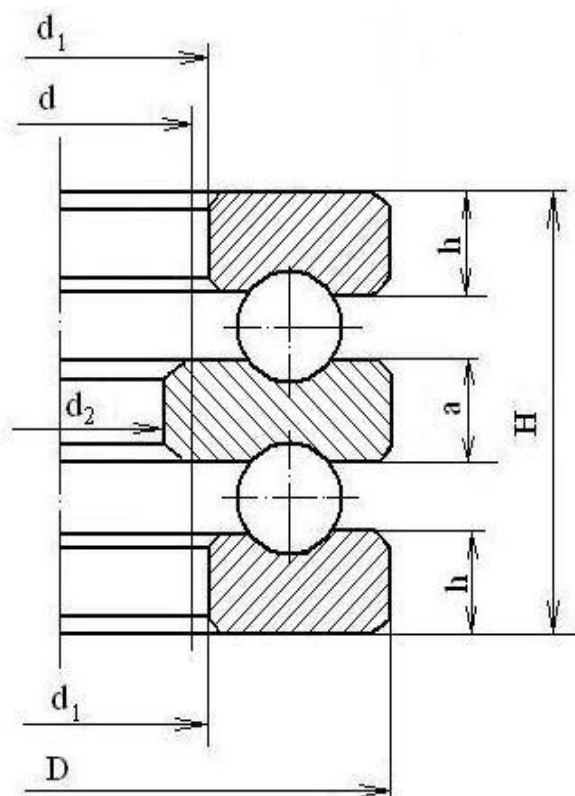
Подшипник шариковый упорный двухрядный
